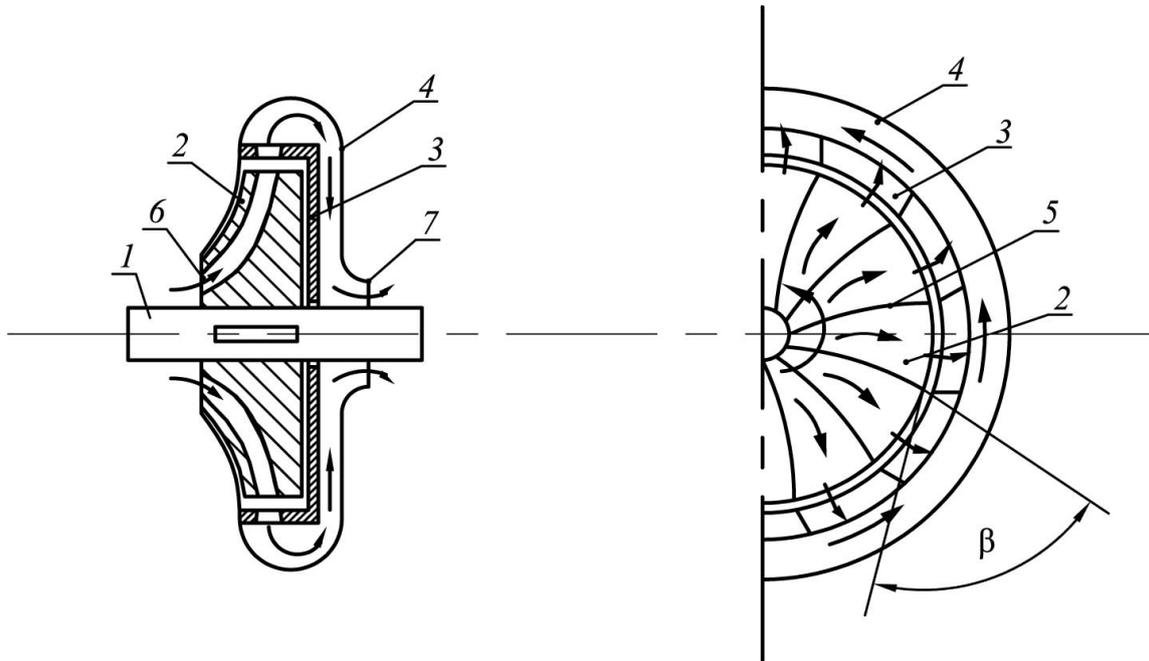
Принципиальный вид одноступенчатого центробежного компрессора:
